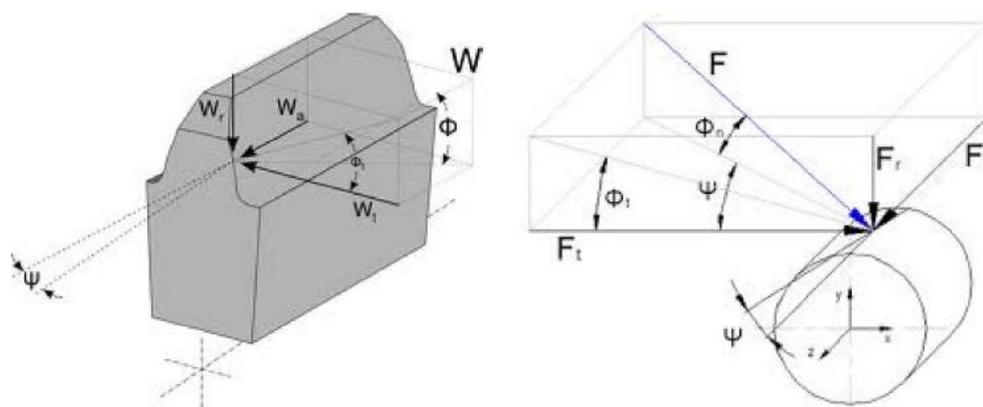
Fuerzas sobre los dientes de un engranaje helicoidal
